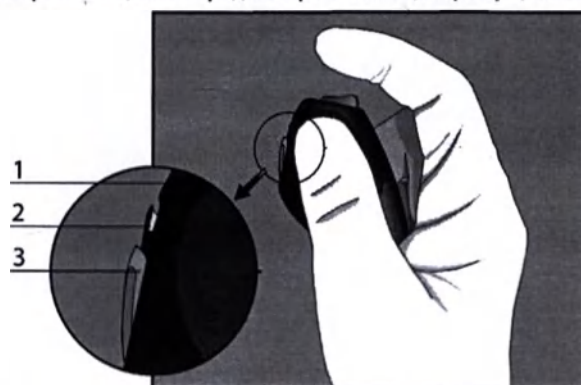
Крепление режущего инструмента, зажимное приспособление не открыто
